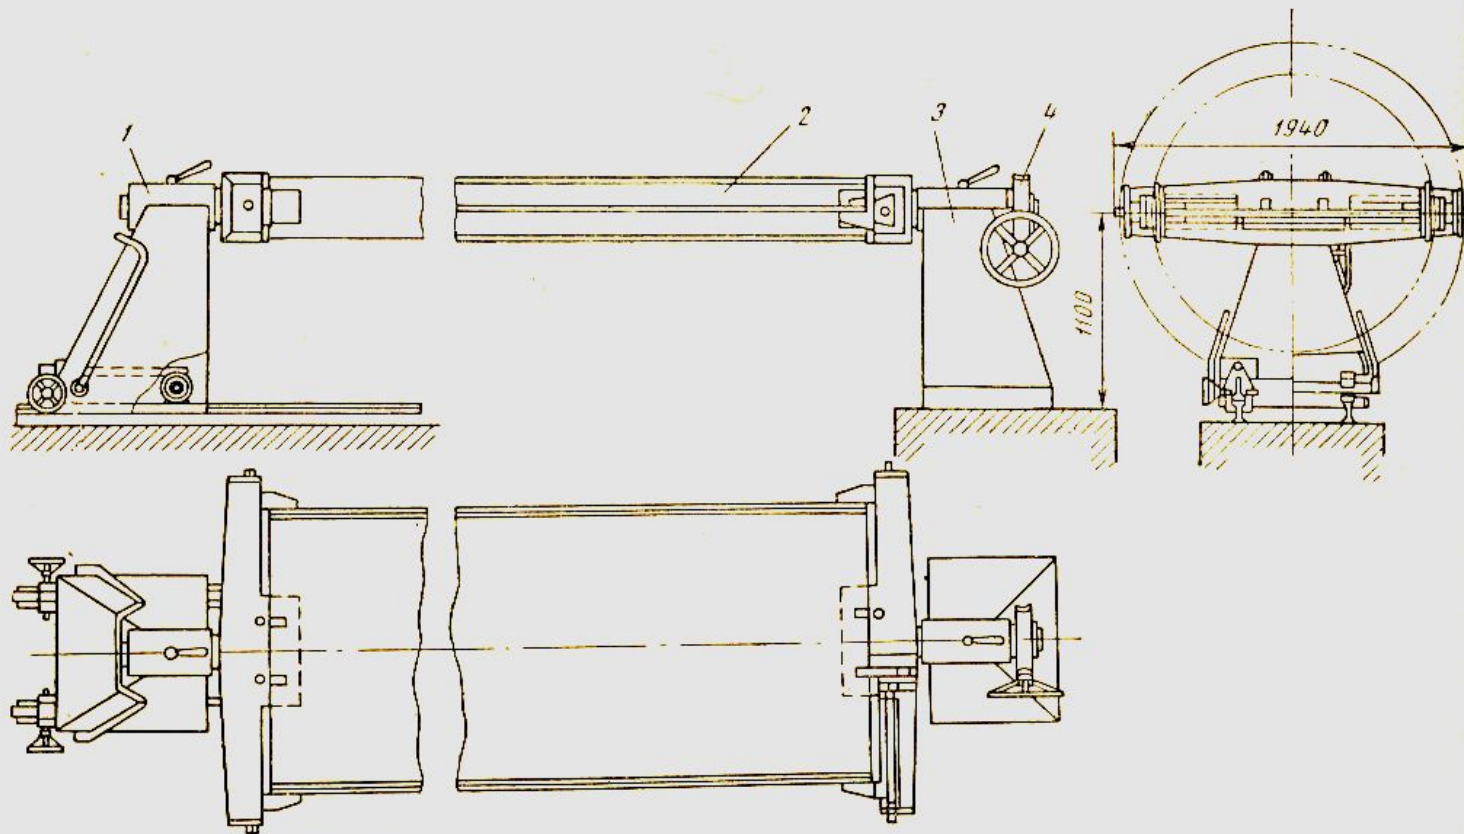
Центральной кантователь для сварных двуглавых балок:
